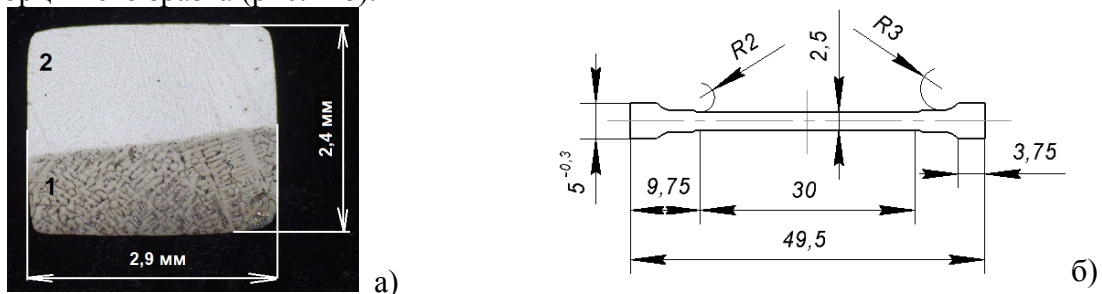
Поперечний переріз робочої ділянки (а) двошарового плоского пропорційного мініатюрного зразка (б). Примітка: 1 – ОМ нікелевого ЖС типу ЖС6; 2 – НМ сплаву Inconel 625
